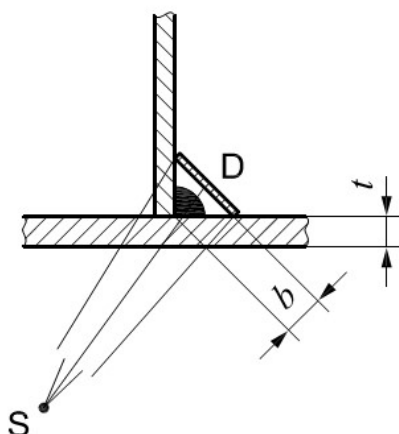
Схема контроля при просвечивании угловых сварных швов
